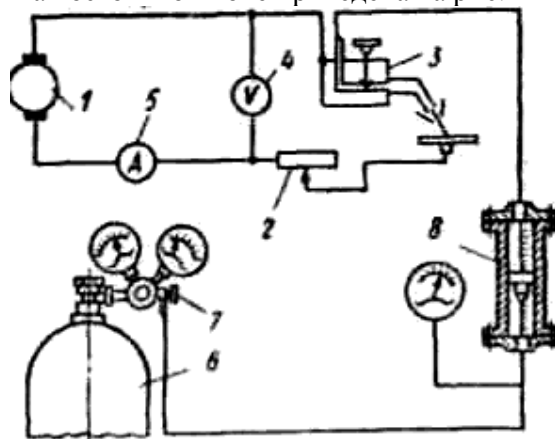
Схема установки для аргоно-дуговой электрической сварки неплавящимся вольфрамовым электродом на постоянном токе: 1 — сварочный генератор постоянного тока; 2 — балластный реостат; 3 — газозлектрическая горелка; 4 — вольтметр; 5 — амперметр; 6 — баллон с газом; 7 — редуктор; 8 — расходомер газа
